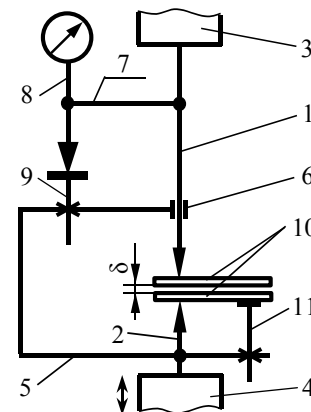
Кінематична схема установки [1]: 1, 2 – верхній і нижній електротримачі; 3, 4 – розривна машина; 5 – скоба; 6 – паз; 7 – кронштейн; 8 – індикатор; 9 – гвинт; 10 – деталь; 11 – фіксатор
